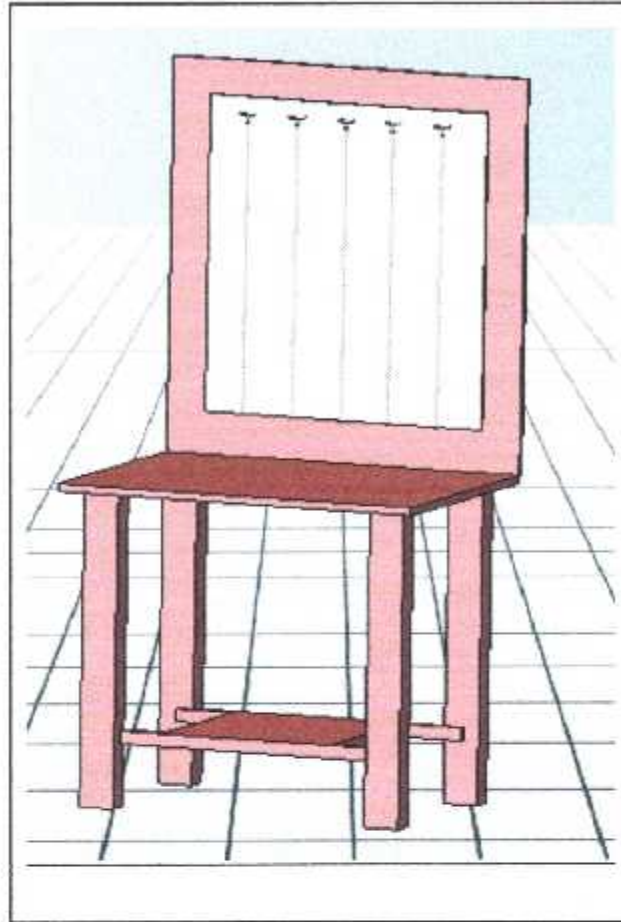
L'assemblage (table + tableau + tube de mesure).
